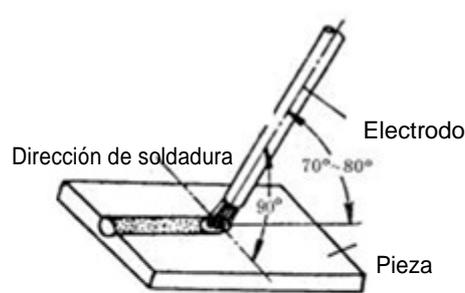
Ángulos del electrodo en soldadura plana
